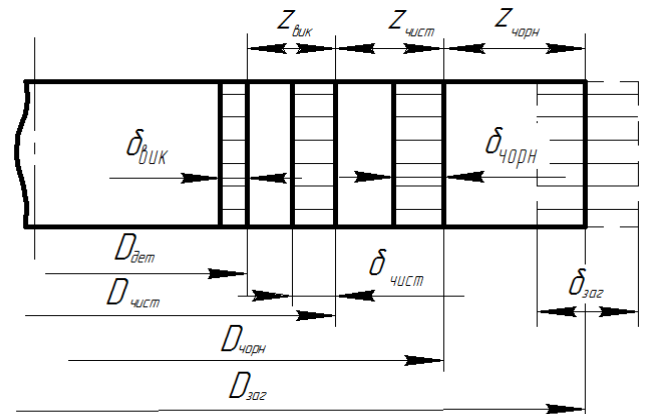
Схема розташування припусків і допусків при багаторазовій обробці зовнішньої поверхні обертання
